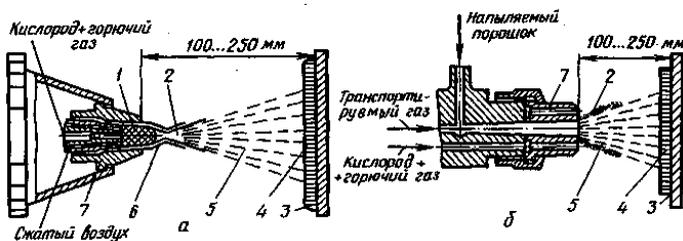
Схема проволочного (а) и порошкового (б) газоплазменного напыления:
